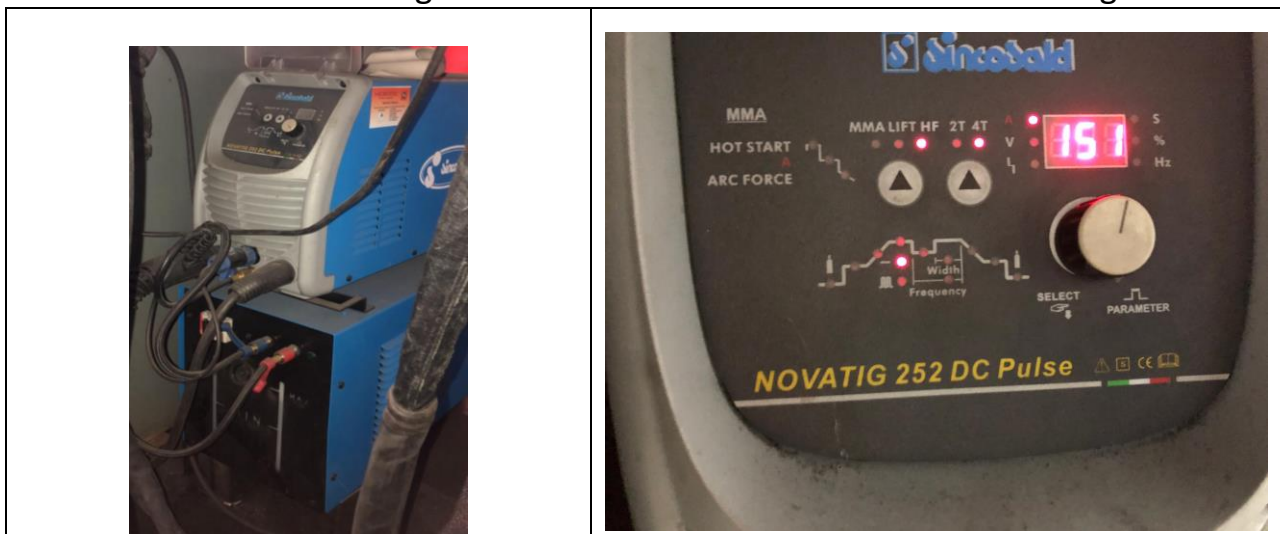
Máquina de soldadura TIG empleada para las pruebas. Panel de control. Fuente: Propia.
